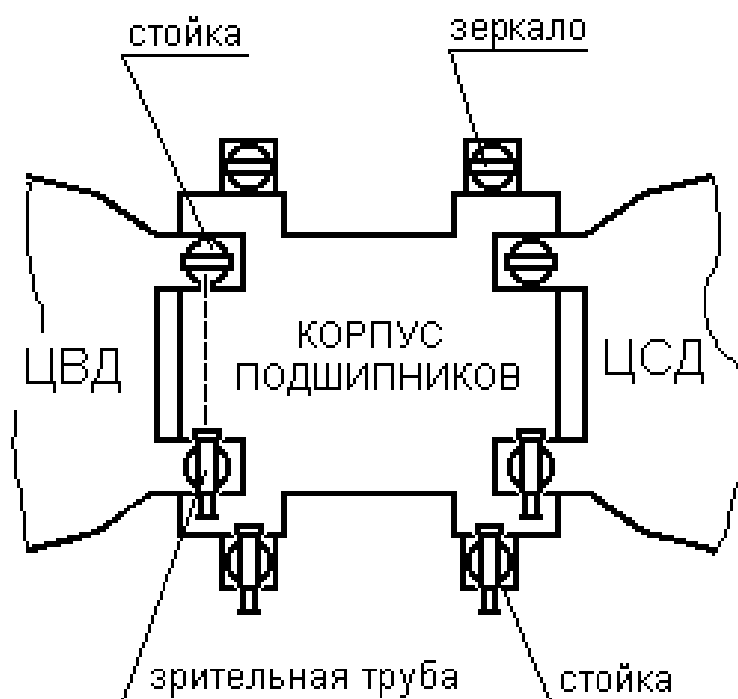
Схема установки оснастки для определения взаимных угловых перемещений лап цилиндров и опорных «крыльев» корпуса подшипника
